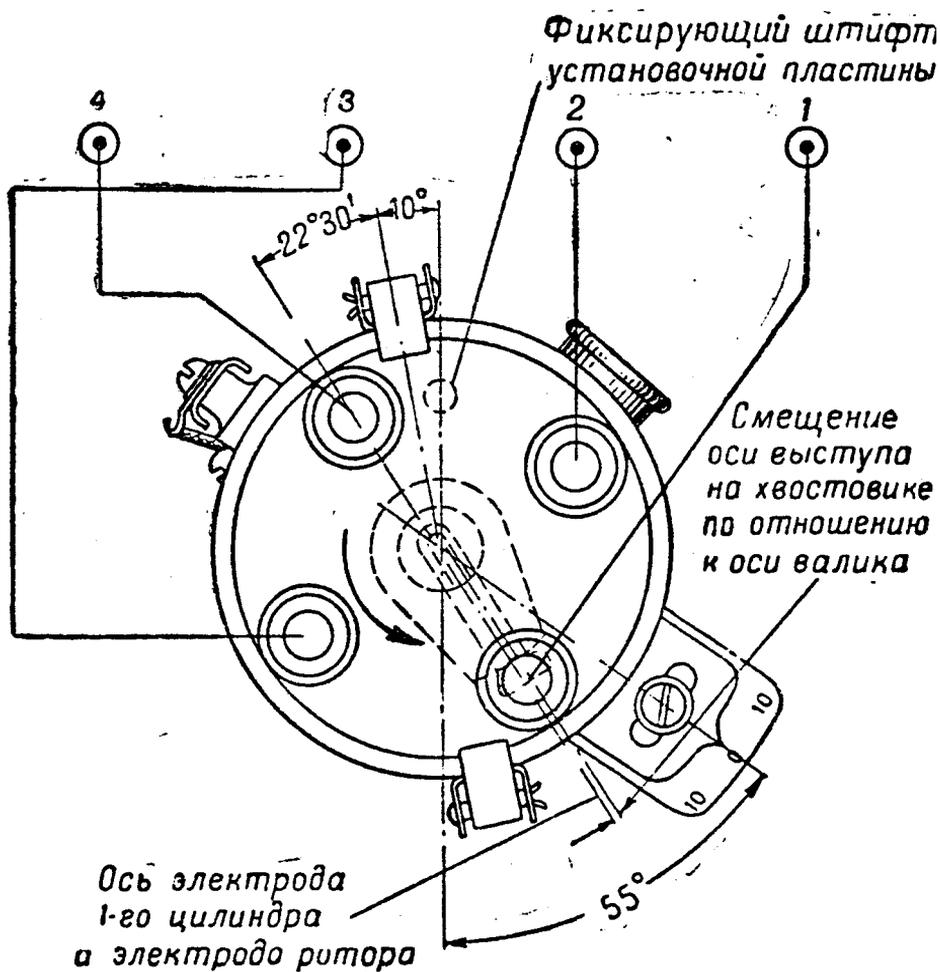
Установка прерывателя-распределителя типа P-15 на двигателе
